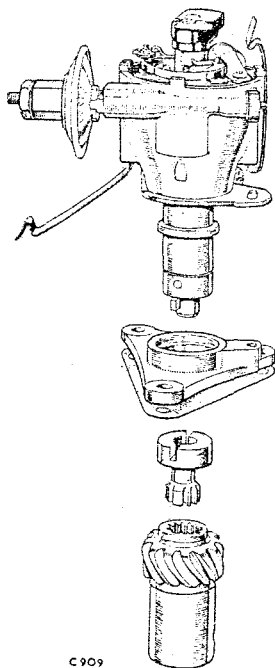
Distribuidor, adaptador y engranaje de transmisión.
